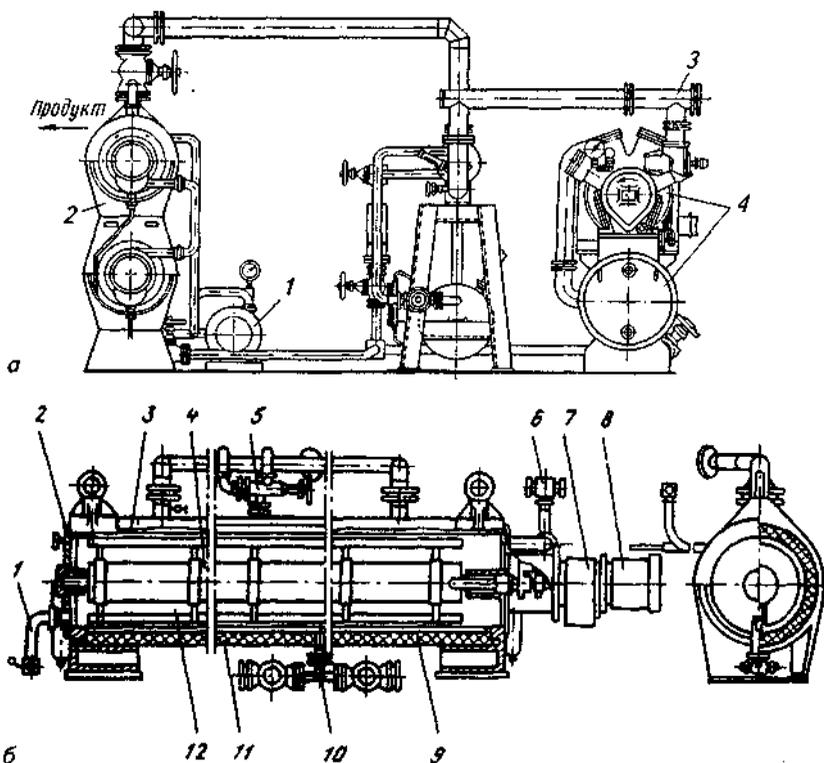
Установка ВУНО-60: а - общий вид (1 - насос; 2 - испаритель-охладитель; 3 - теплообменник; 4 - компрессорно-конденсаторный агрегат); б - испаритель-охладитель ВОИ-58 (разрез общего вида) (1 - патрубок для ввода продукта; 2 - крышка; 3 - корпус; 4 - вал мешалки; 5 - патрубок для отвода хладагента; 6 - выходной патрубок для продукта; 7 - редуктор; 8 - электродвигатель; 9 - изоляция; 10 - патрубок для подвода хладагента; 11 - рубашка; 12 - лопасть мешалки)
